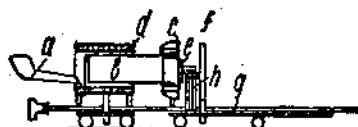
Машина для отливки длинных труб в коротком кокиле.
